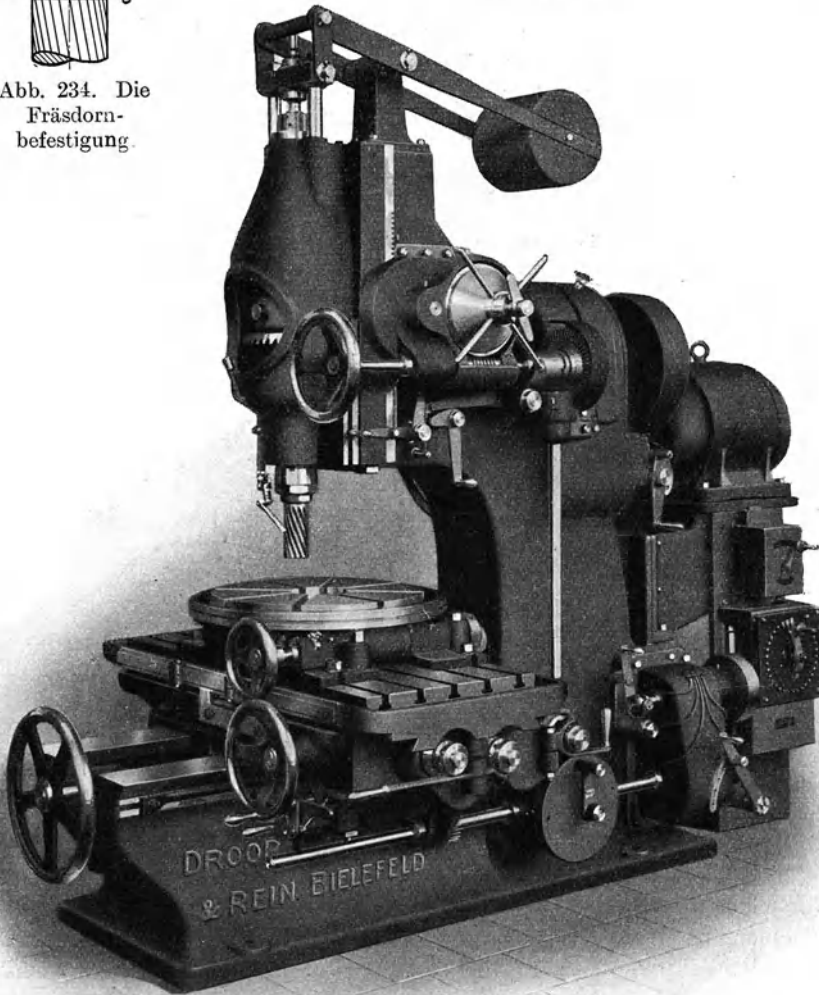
Die große Senkrechtfräsmaschine von Droop & Rein.
